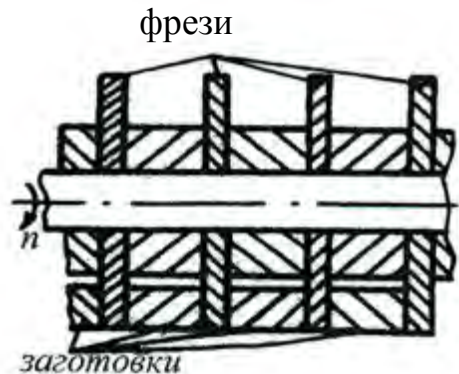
Розрізування прокату декількома фрезами на горизонтально-фрезерному верстаті
